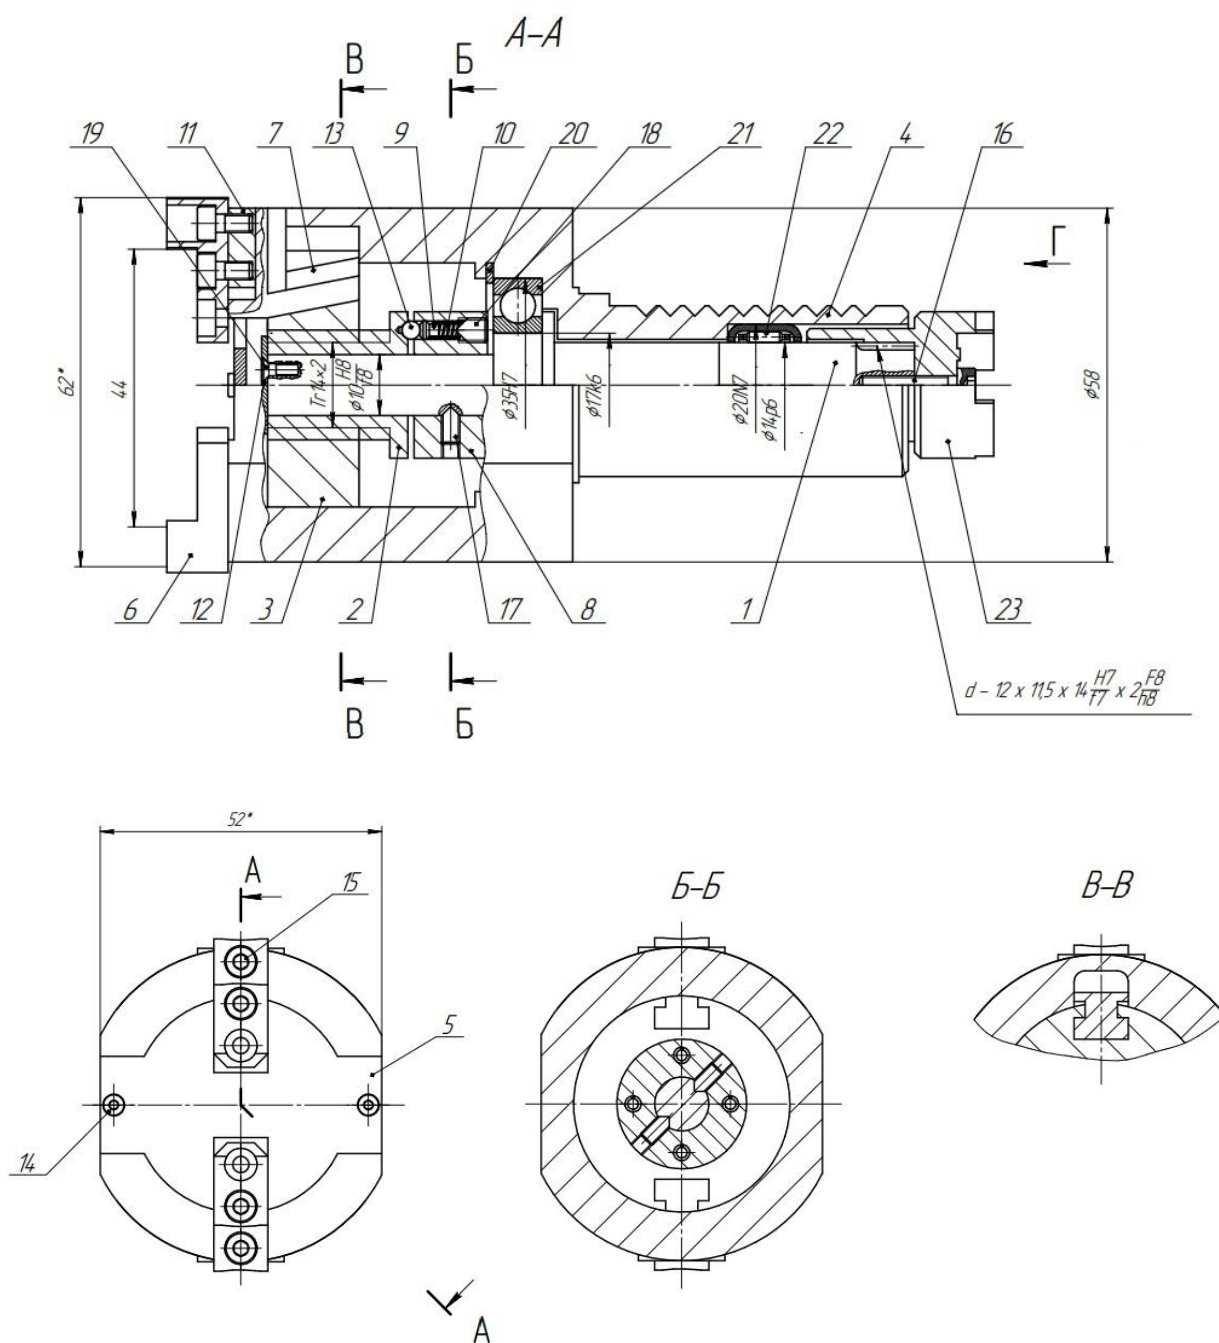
Сборочный чертеж спроектированного барпуллера.
